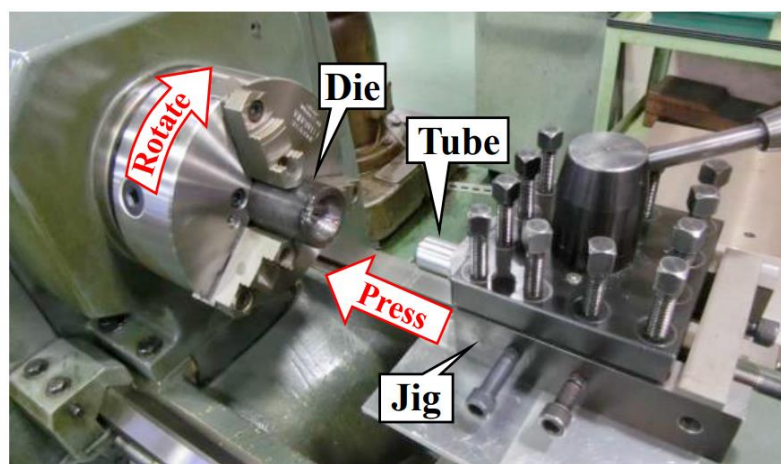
Експериментальна установка процесу обтискання трубчастої заготовки обкочуванням [28]
